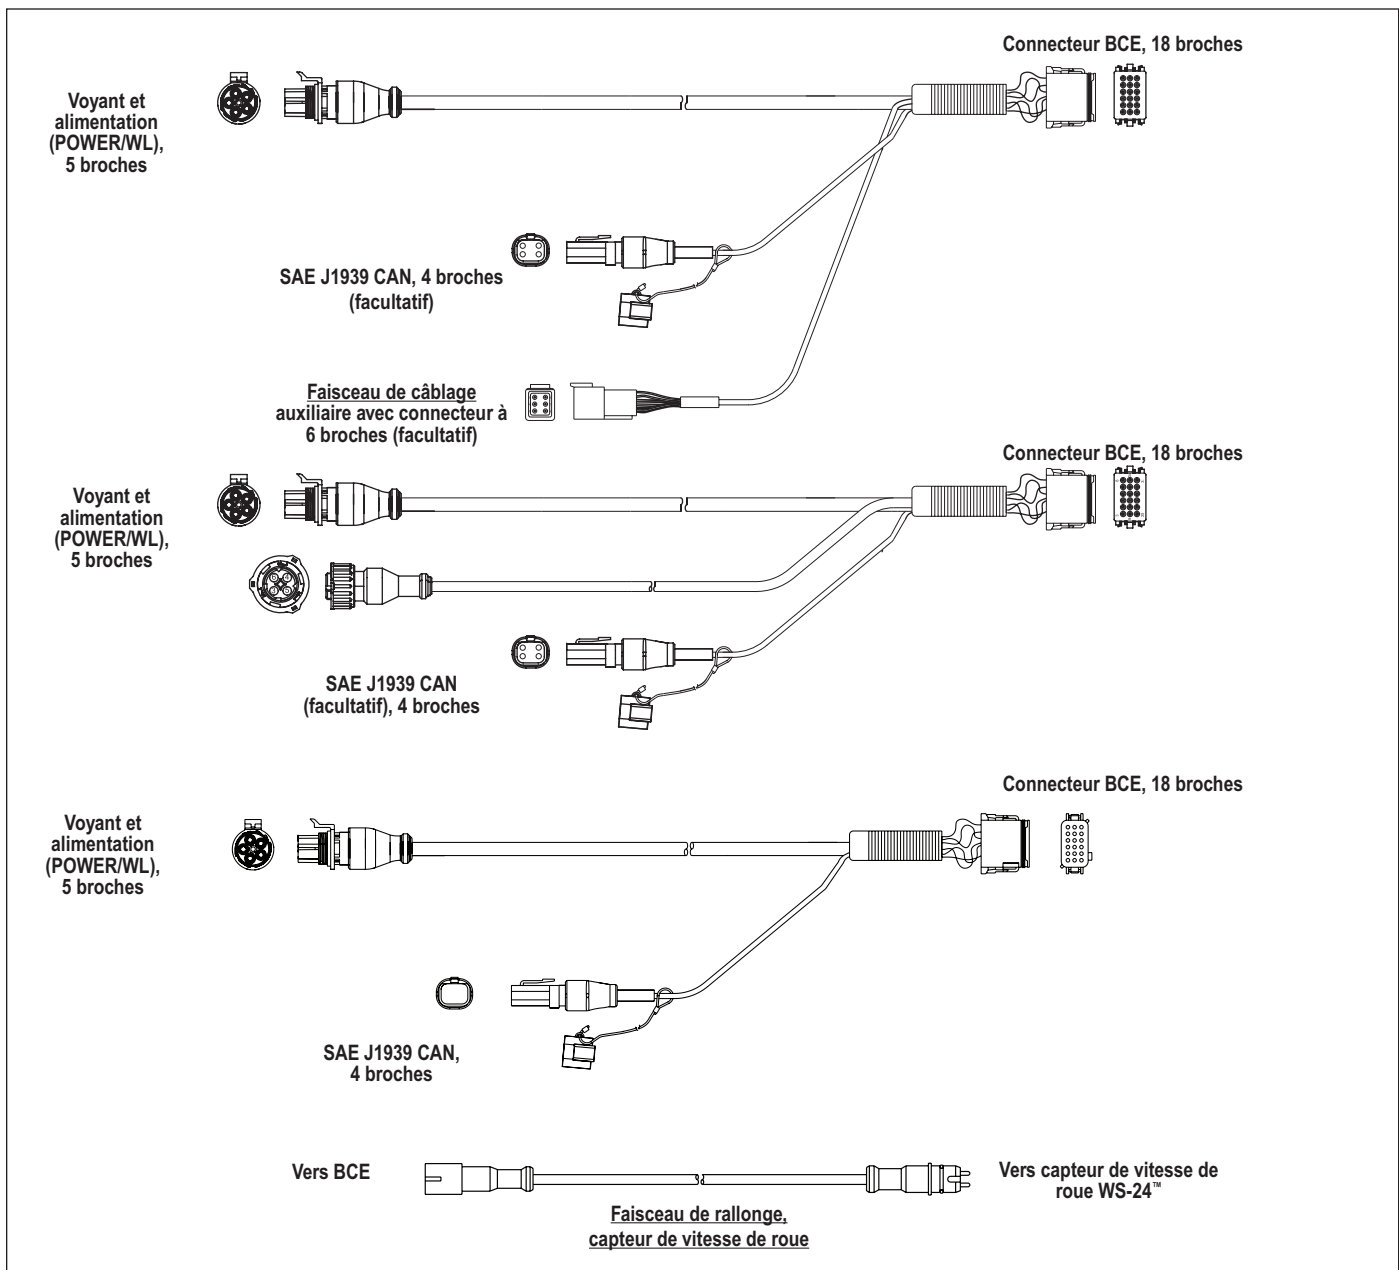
EXEMPLES DE FAISCEAUX DE CÂBLAGE
